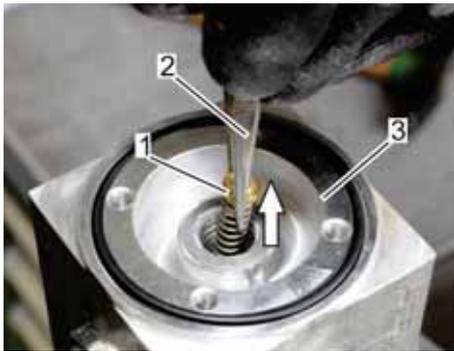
Federausgleichsstück mit Druckfeder entnehmen
